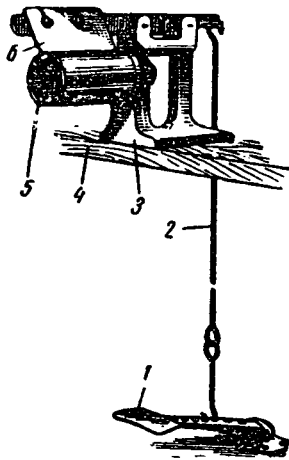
Приспособления для паяния цилиндрических изделий швом внахлестку
